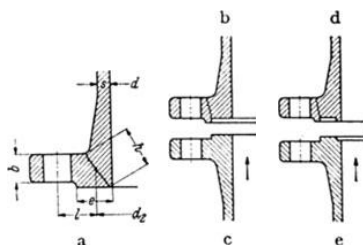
Dichtungsflächen für Flanschen. a) glatte Dichtungsfläche, b) Flansch mit Rücksprung, c) Flansch mit Vorsprung, d) Flansch mit Nut, e) Flansch mit Feder.
